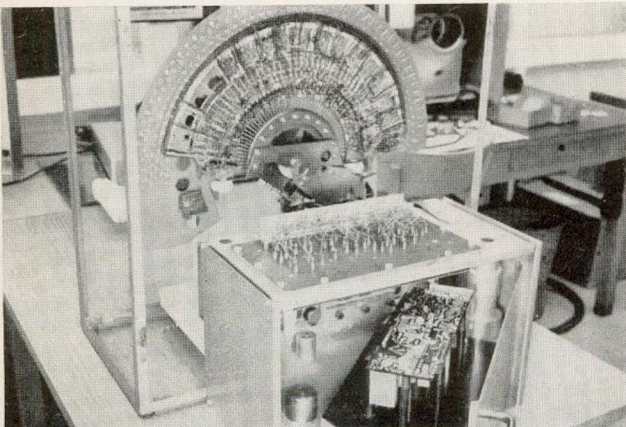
Ansicht eines geöffneten Toleranzprüfgerätes für Leiterplatten. Hinten ist das Schrittschaltwerk, vorn die Aufspannvorrichtung sichtbar
